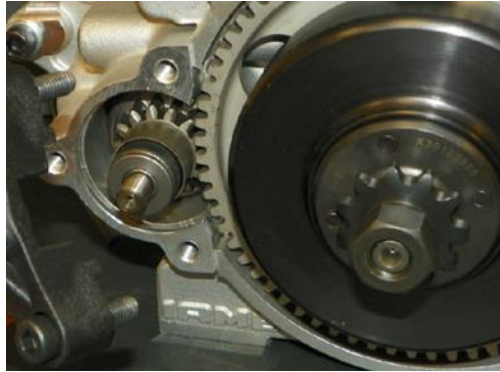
Piñón del motor de arranque y engranaje de arranque (10).
